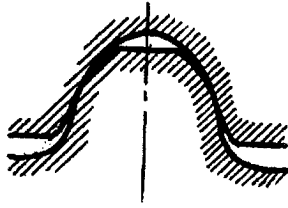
Стандартний вихідний контур для передач Новікова ОЛЗ
